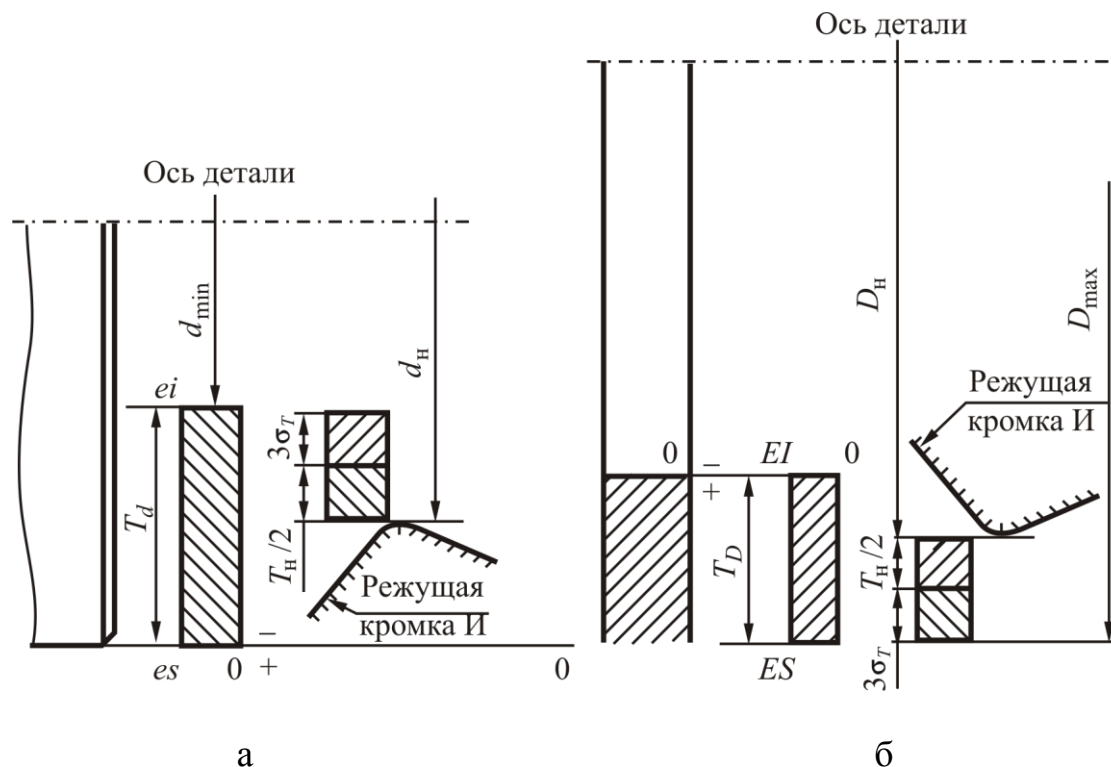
Схема расположения полей допусков на изготовление детали и настройку инструмента: а – при наружном точении; б – при растачивании
